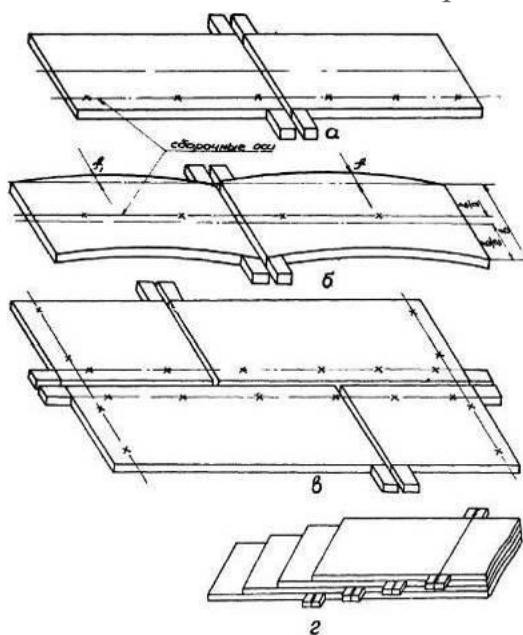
Сборка стыковых соединений листов: а - сборка листов с поперечным стыком; б - сборка универсального проката при наличии саблевидности; в - сборка полотнищ с поперечными и продольными стыками; г - сборка листов пакетом.
